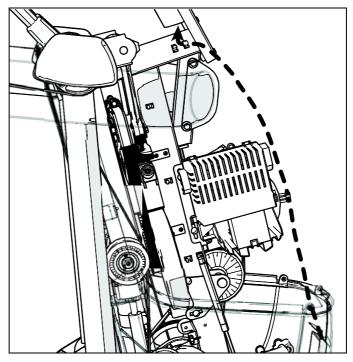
recorrido del cable a través de la estructura hasta la columna central
